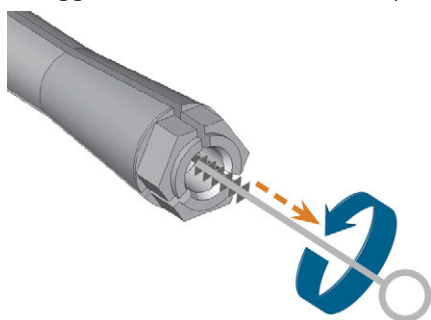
PULIZIA DELLA PINZA DI SERRAGGIO
